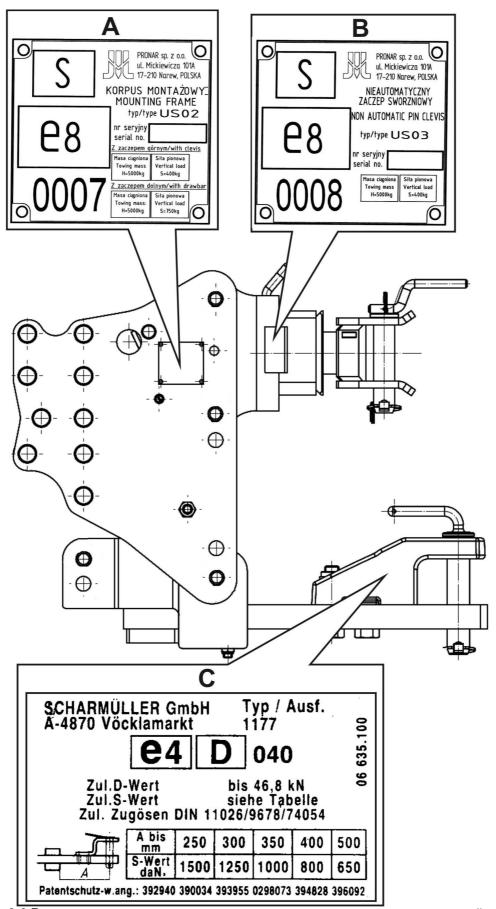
Расположение заводских щитков монтажного корпуса и сцепных устройств. А - монтажный корпус; В - буксирное устройство; С – сцепка для сельскохозяйственных орудий
